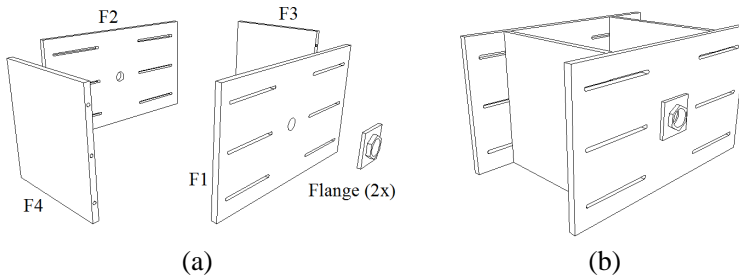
Dispositivo empregado para manutenção da pressão constante dos transdutores – (a) vista explodida; (b) dispositivo montado
